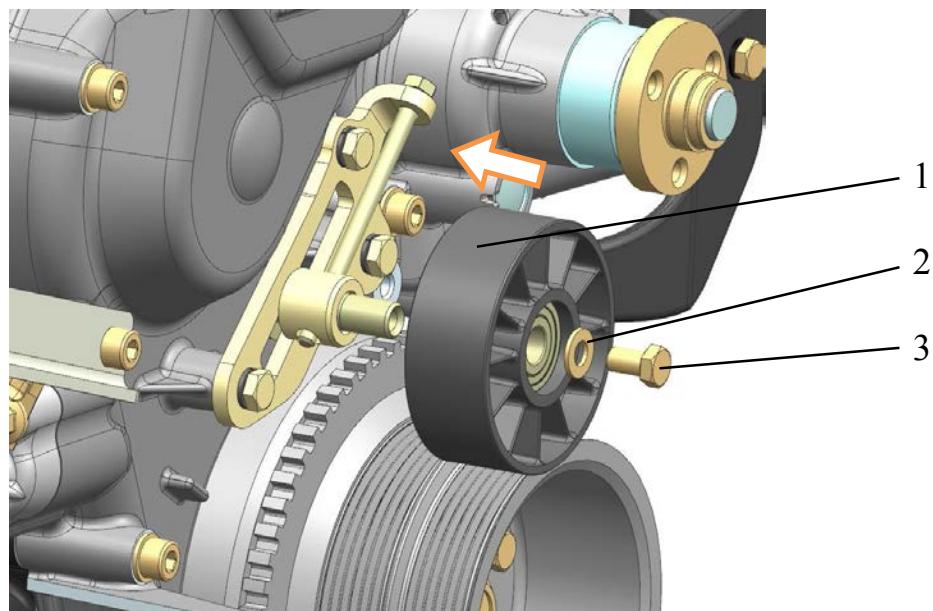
Установка натяжного ролика ремня привода водяного насоса и генератора:
